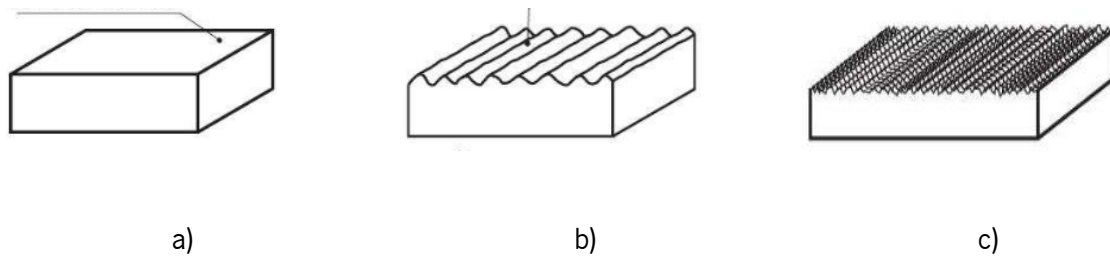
Ilustração de avaliação do estado das superfícies. a) Superfície geométrica; b) Superfície real; c) Superfície efetiva (adaptado [12]).
